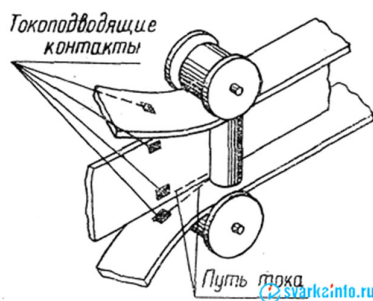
Схема безперервного процесу виготовлення балки з трьох полос за допомогою ВЧ зварювання
